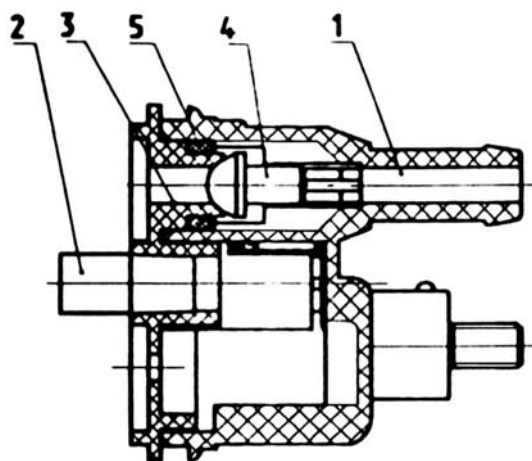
Выходная крышка ЭБН: 1 – корпус выходной крышки с контактной группой; 2 – щетки (2 шт.); 3 – щеткодержатель; 4 – обратный клапан; 5 – уплотнительное кольцо
